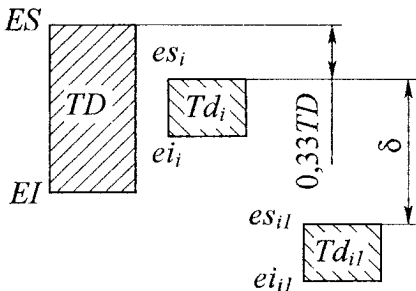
Схема відносного положення допуску розвертки і деталі
